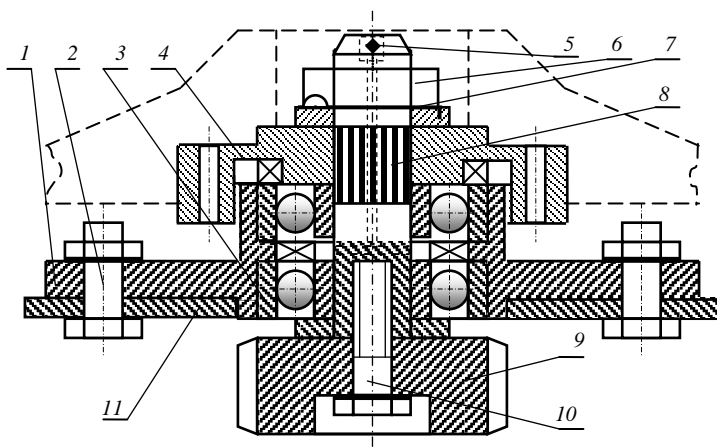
Схема привода роторов рабочего органа многороторной косилки: 1 – стакан; 2 – болты; 3 – подшипники; 4 – фланец; 5 – пресс-масленка; 6 – гайка; 7 – шайба; 8 – вал ротора; 9 – приводная шестерня; 10 – болт; 11 – верхняя часть корпуса редуктора
